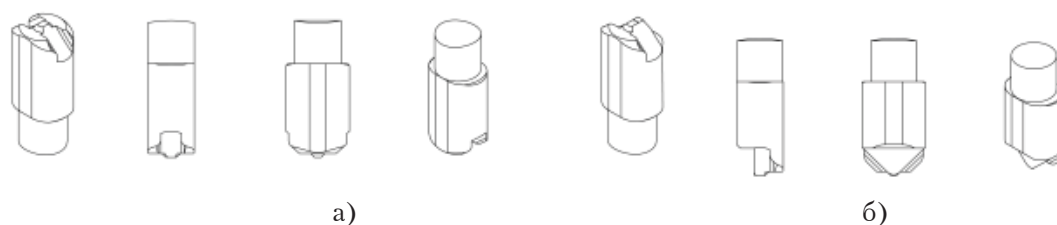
Зовнішній вигляд штифта Integrator™ (а – двобічний; б – однобічний)
